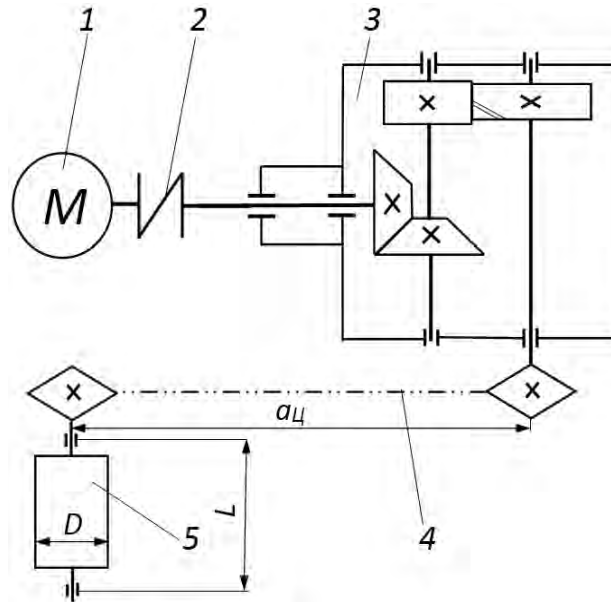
Схема привода ленточного конвейера (вид сверху): 1 – асинхронный электродвигатель; 2 – муфта упругая втулочно-пальцевая; 3 – редуктор коническо-цилиндрический (расположение конической шестерни симметрично относительно стенок корпуса редуктора); 4 – цепная передача; 5 – приводной вал с барабаном
